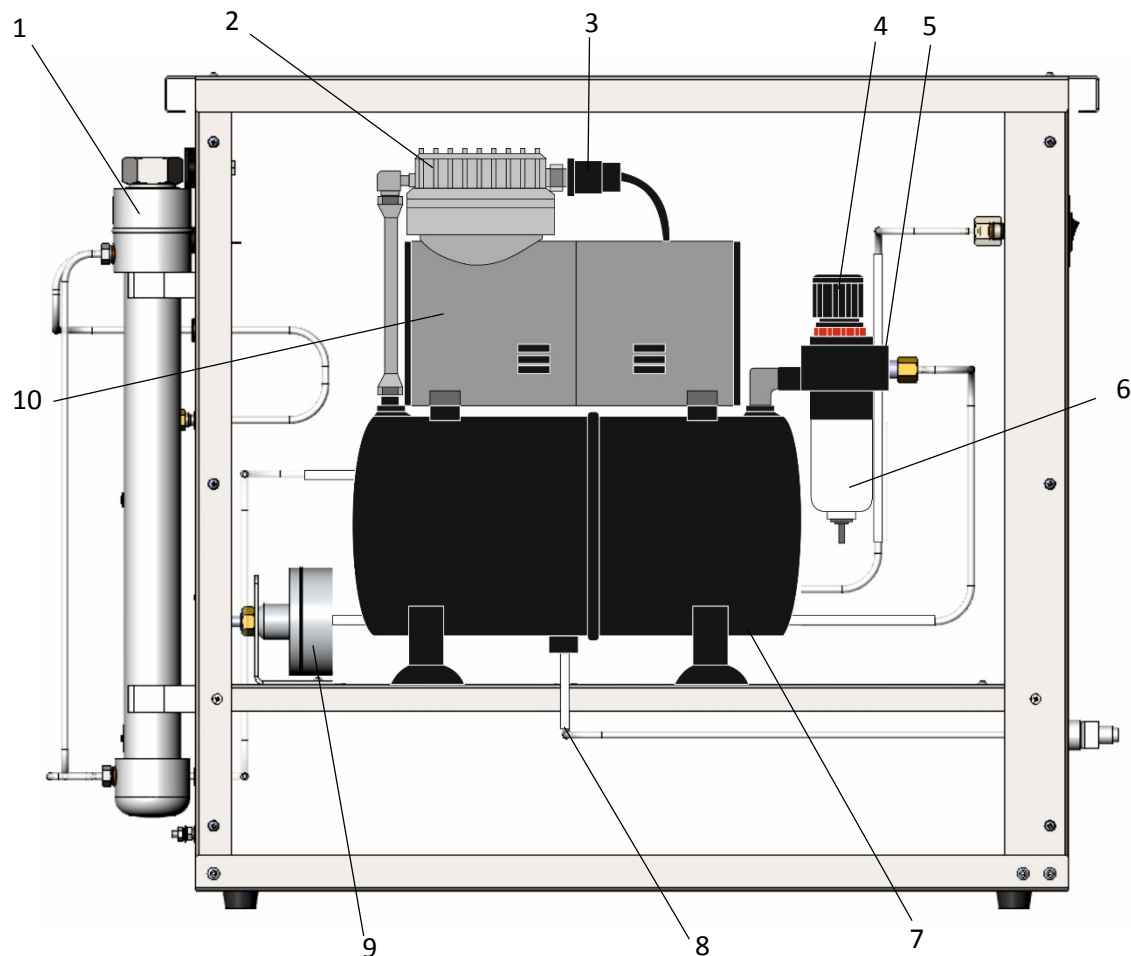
Компрессор – вид слева со снятыми боковыми крышками. 1 – Фильтры; 2 – рабочая камера; 3 – Реле давления; 4 – Регулятор давления; 5 – Манометр; 6 – Фильтр с конденсатоотводчиком; 7 – Ресивер; 8 – Трубка слива конденсата из ресивера; 9 – Регулятор давления второй ступени; 10 – электродвигатель.
